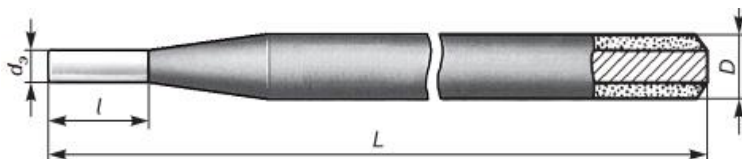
Покрытый электрод для ручной дуговой сварки:
